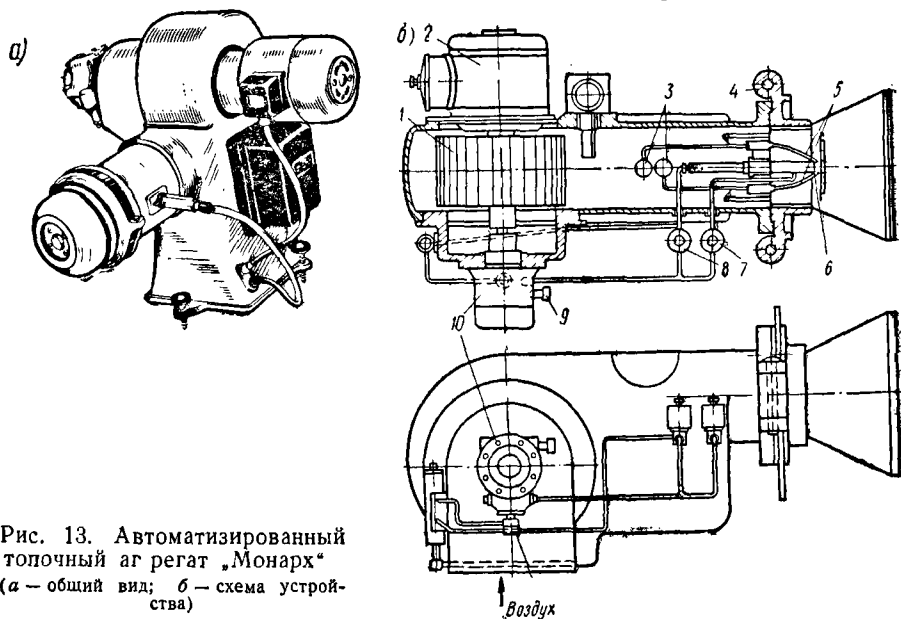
Автоматизированный топочный агрегат „Монарх“ (а — общий вид; б — схема устройства)
